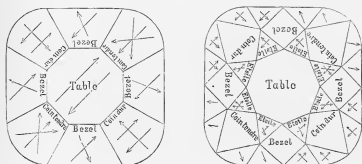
Mise en huit et brillantage des pierres deux pointes.
